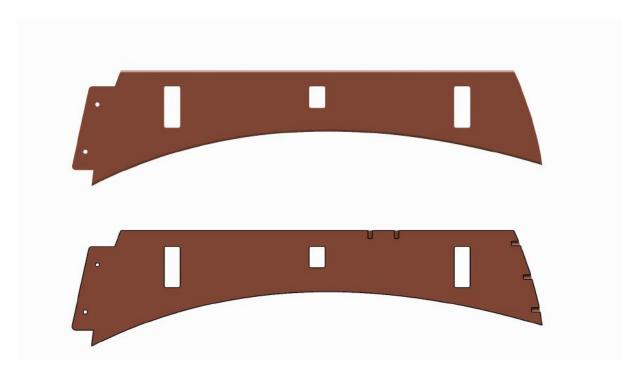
Detalhe em corte Estrutura Lateral - Furos para cavilhas
